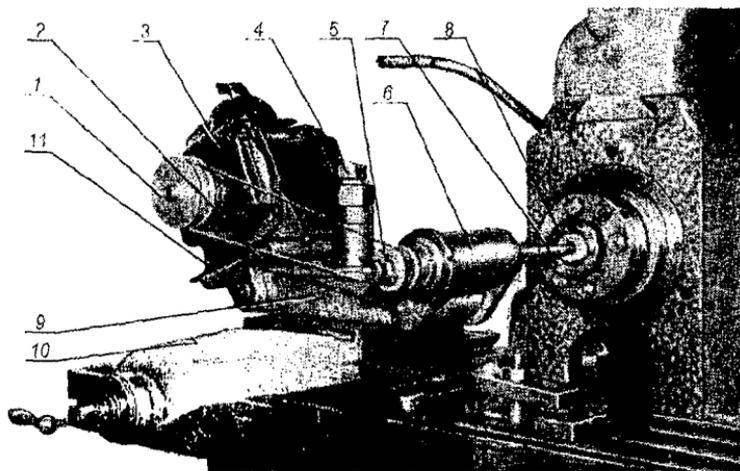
Приспособление для шлифования отверстий шпинделей
